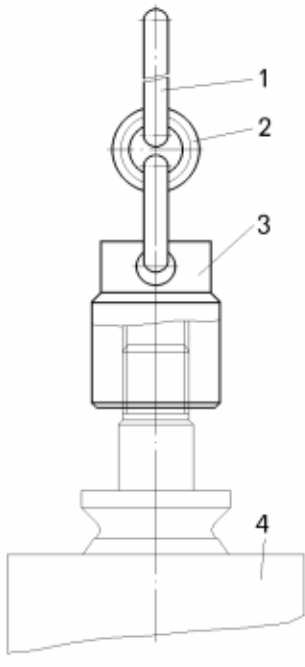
Приспособление для снятия и установки цилиндров подвески (используется как навесное оборудование к погрузчику):
